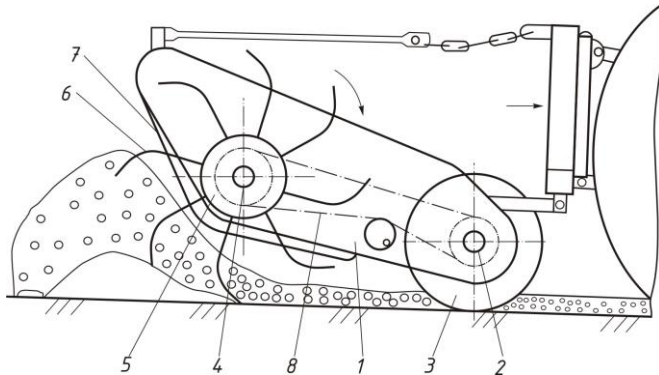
Схема ворошилки стрічок льону: 1 – рама; 2 – вал коліс; 3 – опорно-приводні колеса; 4 – вал дисків; 5 – диски; 6 – зуб; 7 – знімна решітка; 8 – ланцюгова уповільнювальна передача
